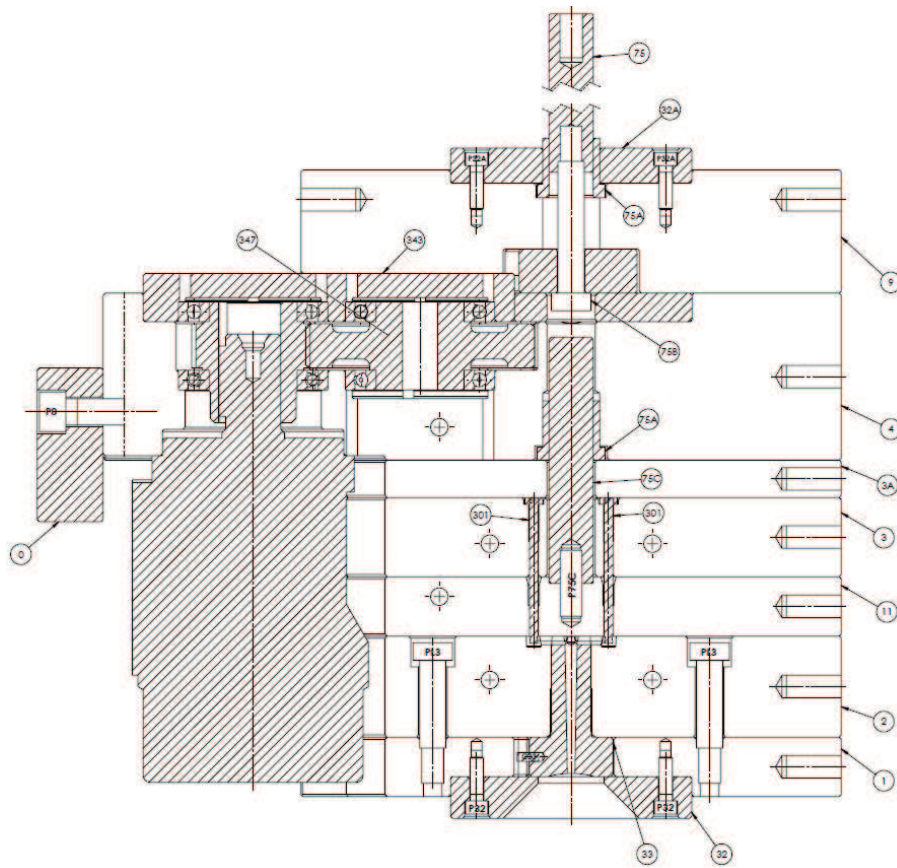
Molde de injeção com indicação dos vários componentes do molde 828 (vista em corte: seção A-A (desenho 2D final para montagem)).
